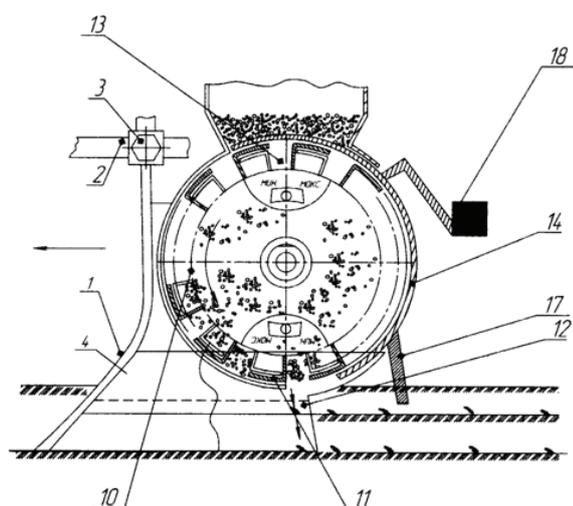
Сошник для разноуровневого внесения удобрений: 1- щелеобразователь; 2 – стойка; 3 – винт; 4 – щит; 5 – ось; 6 – втулка; 7 – диск; 8 – кольцо; 9 - бункер для удобрений; 10 – пластина; 11 - Г-образная пластина; 12 - пластина-разделитель; 13 - прямоугольные ячейки; 14 – кожух; 15 - указатель дозы; 16 – гайка; 17 – зуб; 18 - груз
